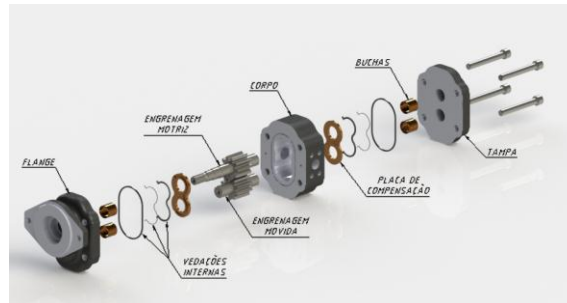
Bomba hidráulica de engrenagens externas, vista explodida.
